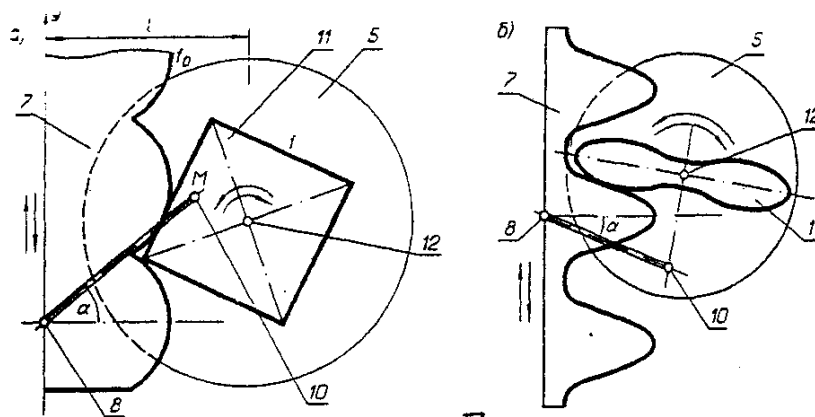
Конструкція верстатів для фрезерування криволінійних профілів
